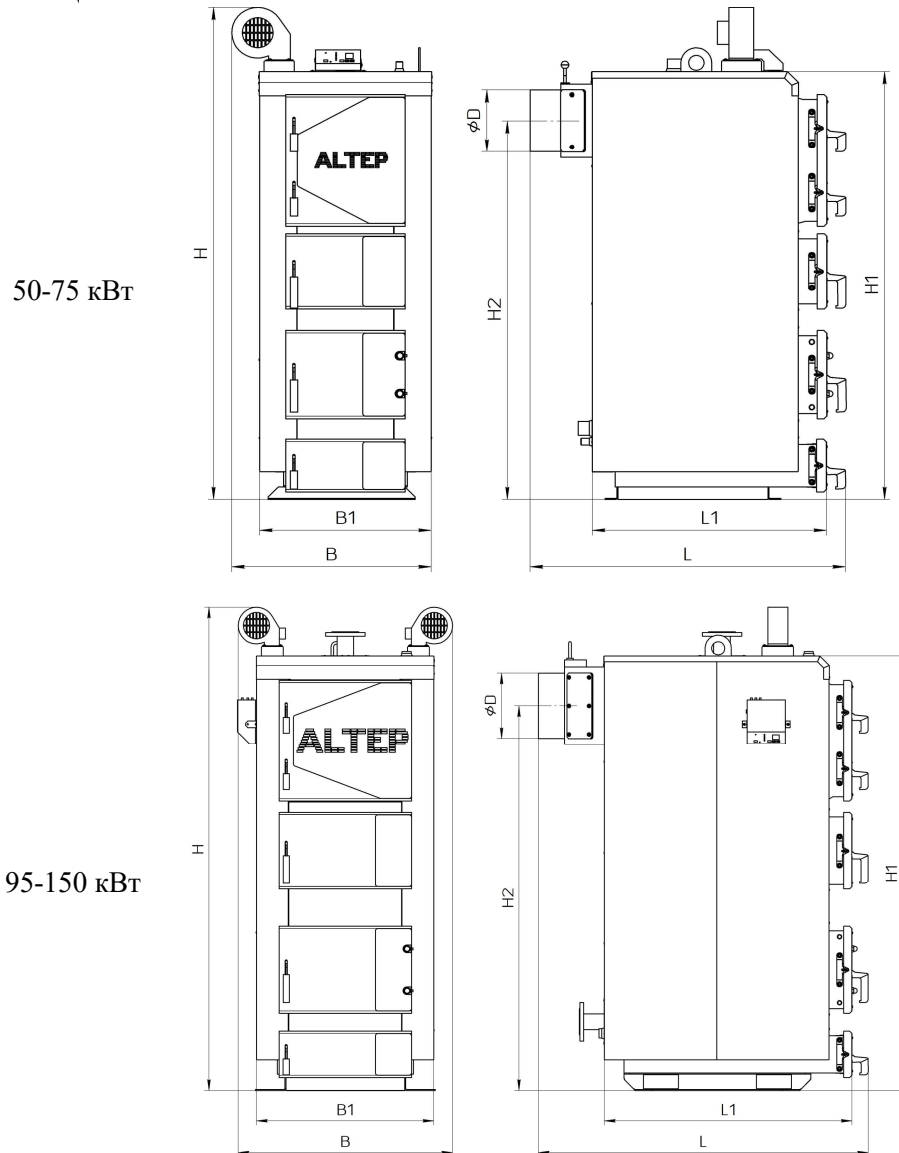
Габаритный чертёж котла типа КТ-2Е-N (NM)
